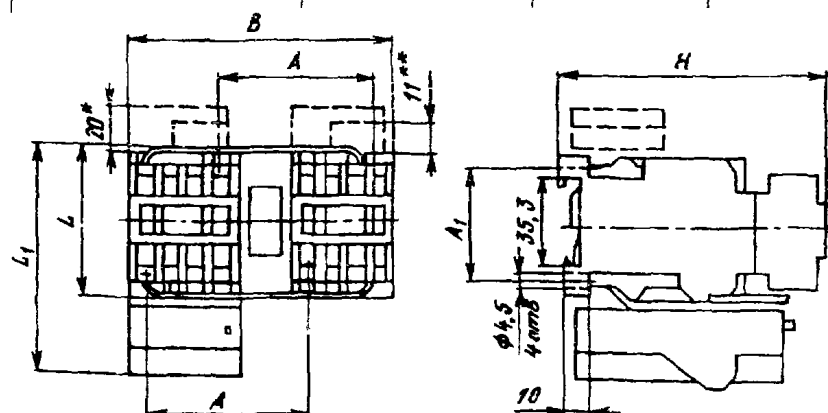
Габаритные и установочные размеры пускателя реверсивного ПМ12-010 степени защиты IP00 и IP20
